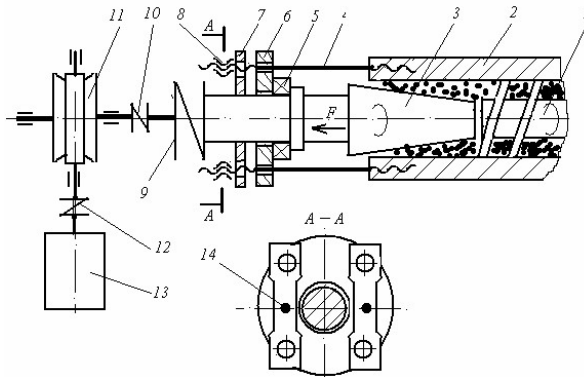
Кінематична схема вузла для вимірювання напірного тиску на ротор головки подрібнення екструдера: 1 – черв'як; 2 – матеріальний циліндр; 3 – конусна головка; 4 – направляючі шпильки; 5 – упорний підшипник; 6 – опорний диск; 7 – вимірювальні балки; 8 – регулюючі гайки; 9 – шліцева муфта; 10, 12 – втулково-пальцеві муфти; 11 – черв'ячний редуктор; 13 – електродвигун постійного струму; 14 – тензодатчики
